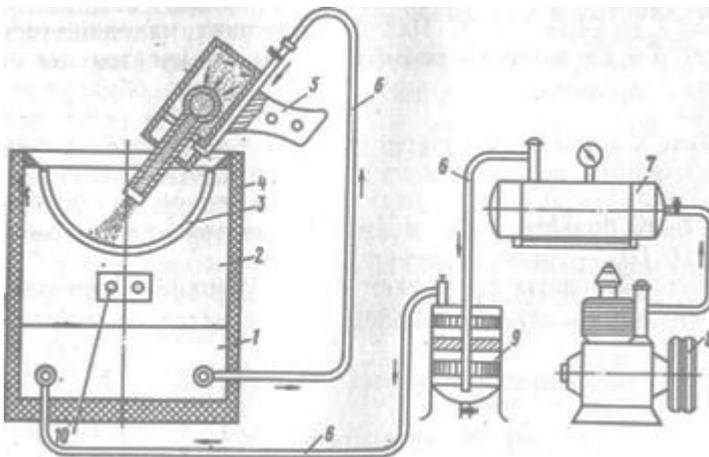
Установка для напыления капрона на вкладыш подшипника:
